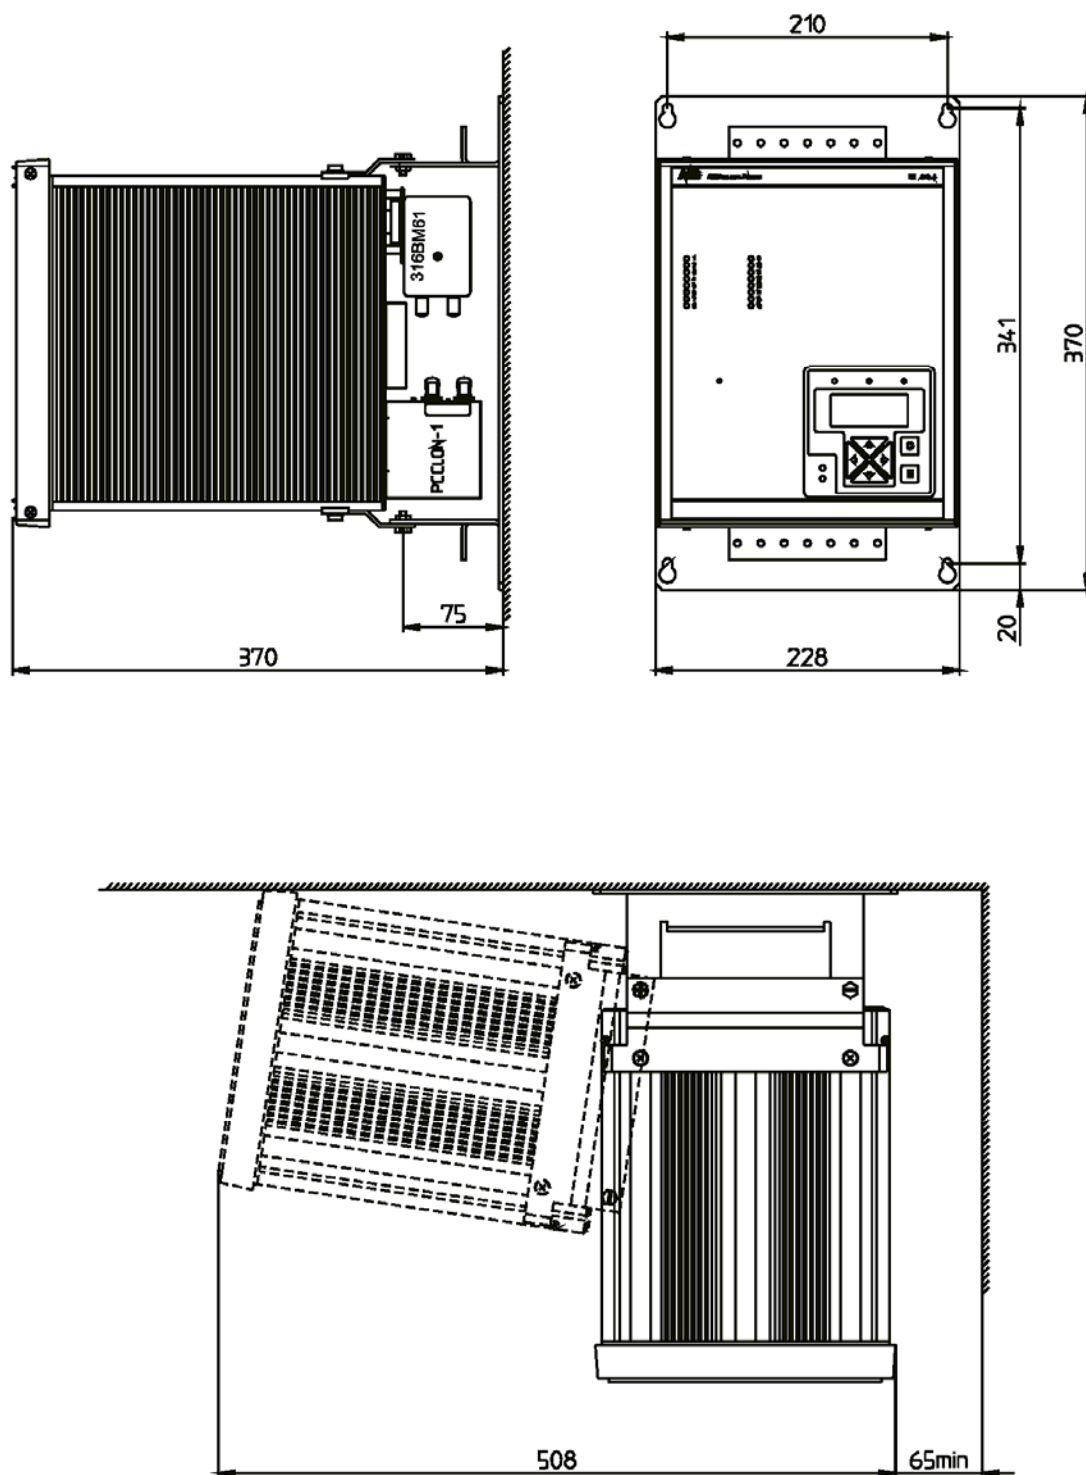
Навесной монтаж, корпус может поворачиваться влево, заднее присоединение, корпус размером N1
